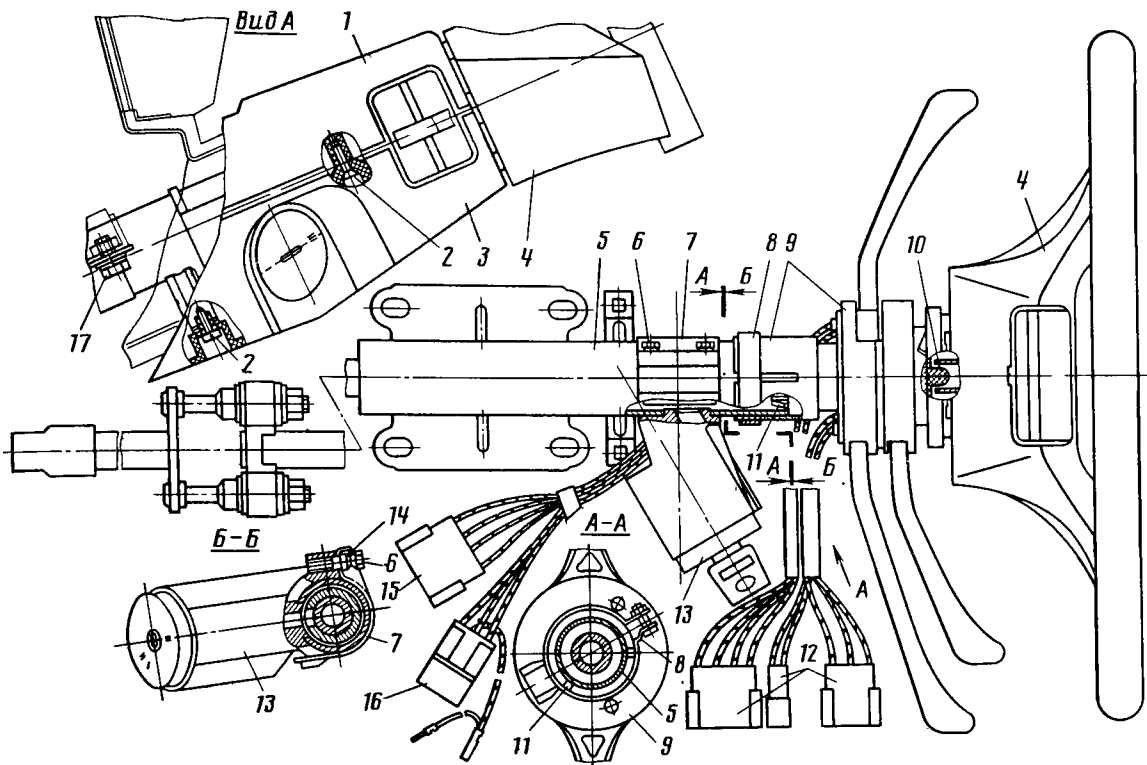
Опора вала в сборе с выключателем зажигания, рулевым колесом и переключателем:
